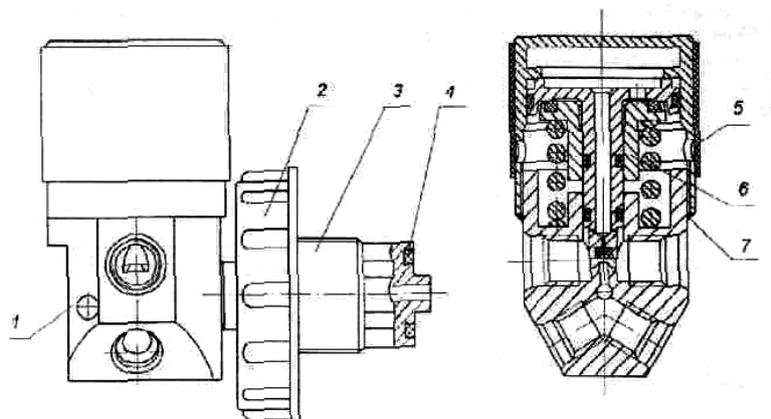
Редуктор: 1 – корпус редуктора; 2 – маховичок; 3 – резьбовой штуцер; 4 – кольцо 9В8.684.909; 5 – манжета; 6 – предохранительный клапан; 7 – пломба
